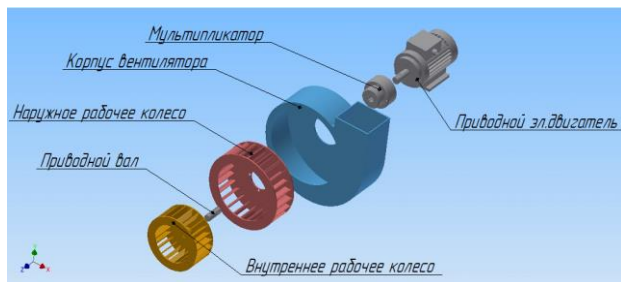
Центробежная турбомашина с коаксиальным расположением рабочих колес
